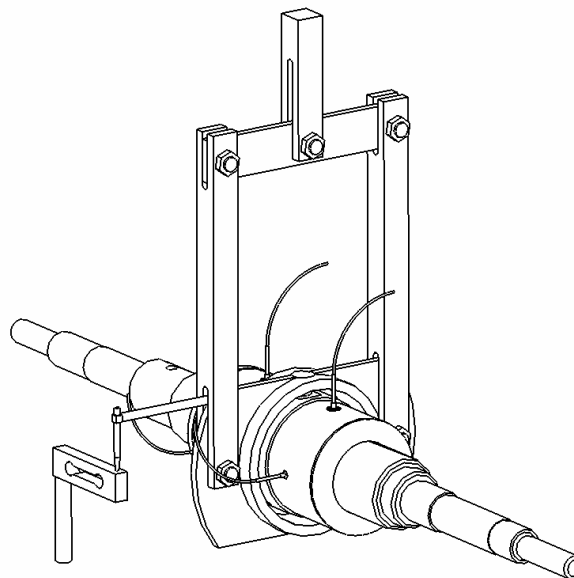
Detalhe do dispositivo para medição do torque viscoso.
